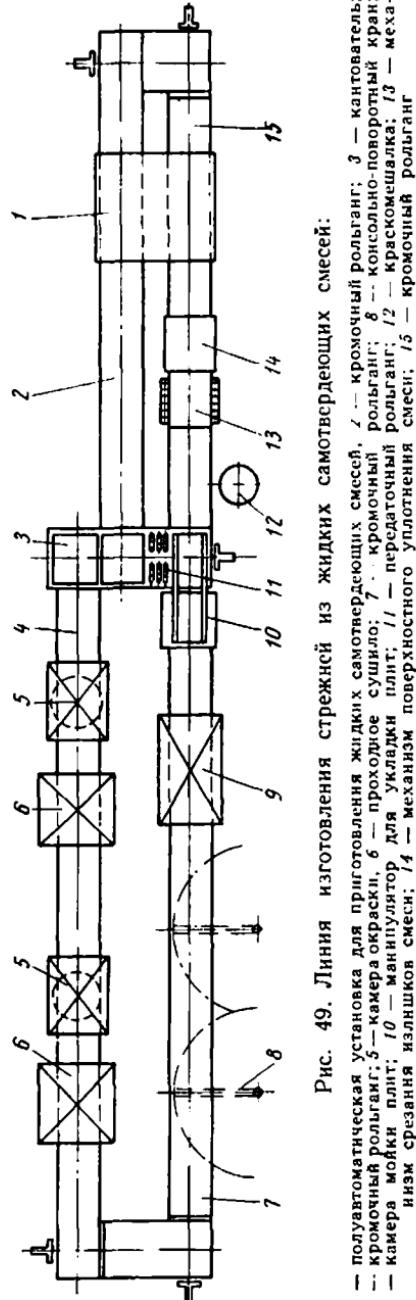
Линия изготовления стержней из жидких самотвердеющих смесей:
